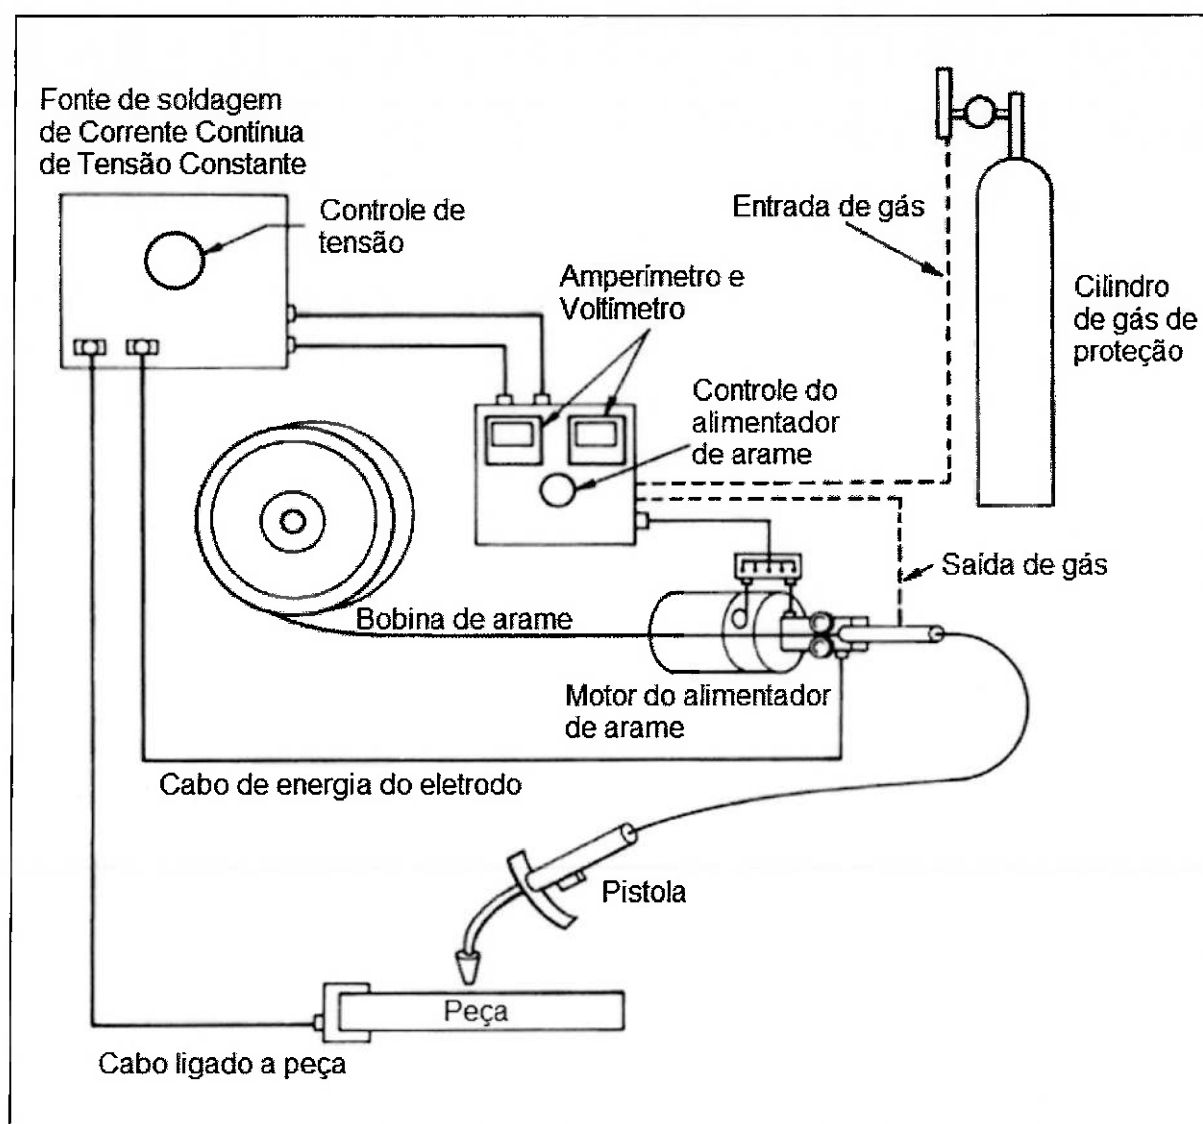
Esquema do equipamento de soldagem AT [15]
